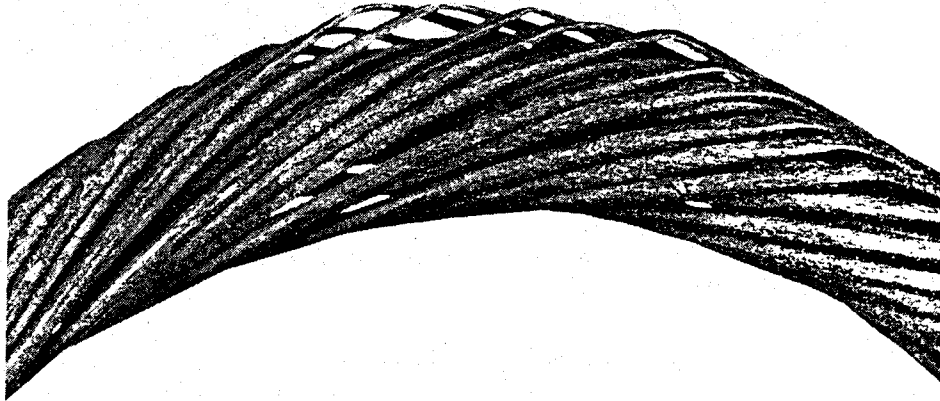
Drahtseil mit durch Korrosion und Abrieb gelockerten Drähten
